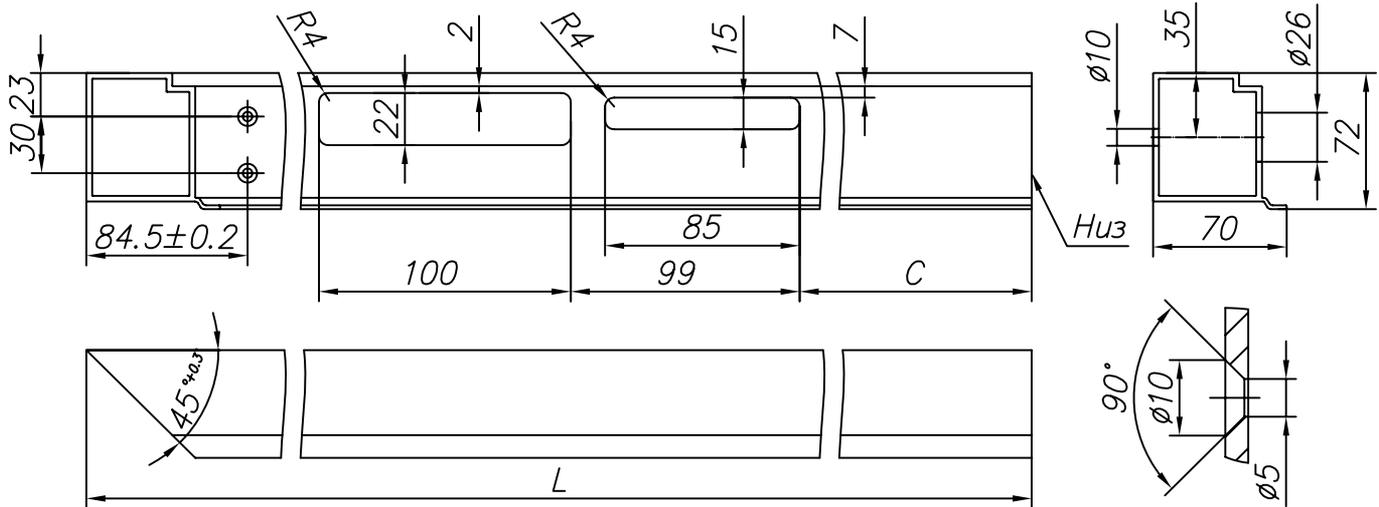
Изготовление столба притвора с пазом для автоматической защелки 118WE для калитки с перекладиной (открывание влево)
